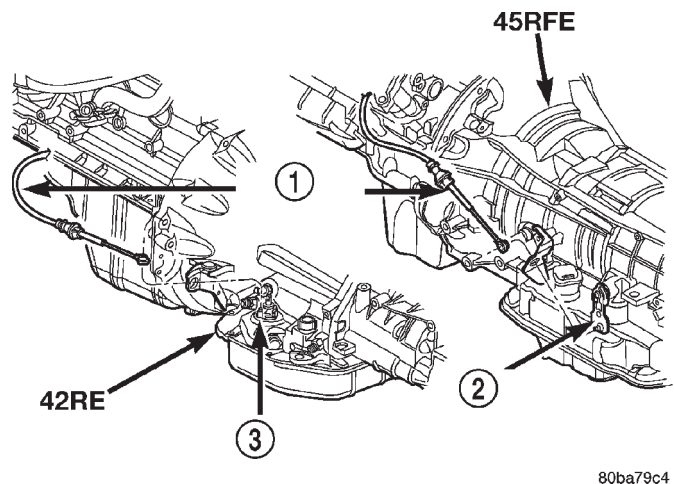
Desmontaje del cable de cambio de marcha de la transmisión
